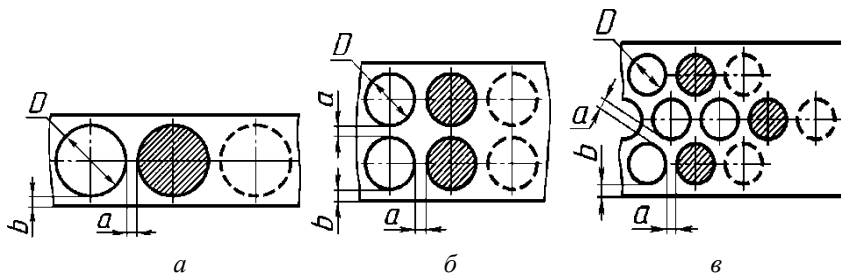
Способы раскроя круглых заготовок: *a* – однорядный;
